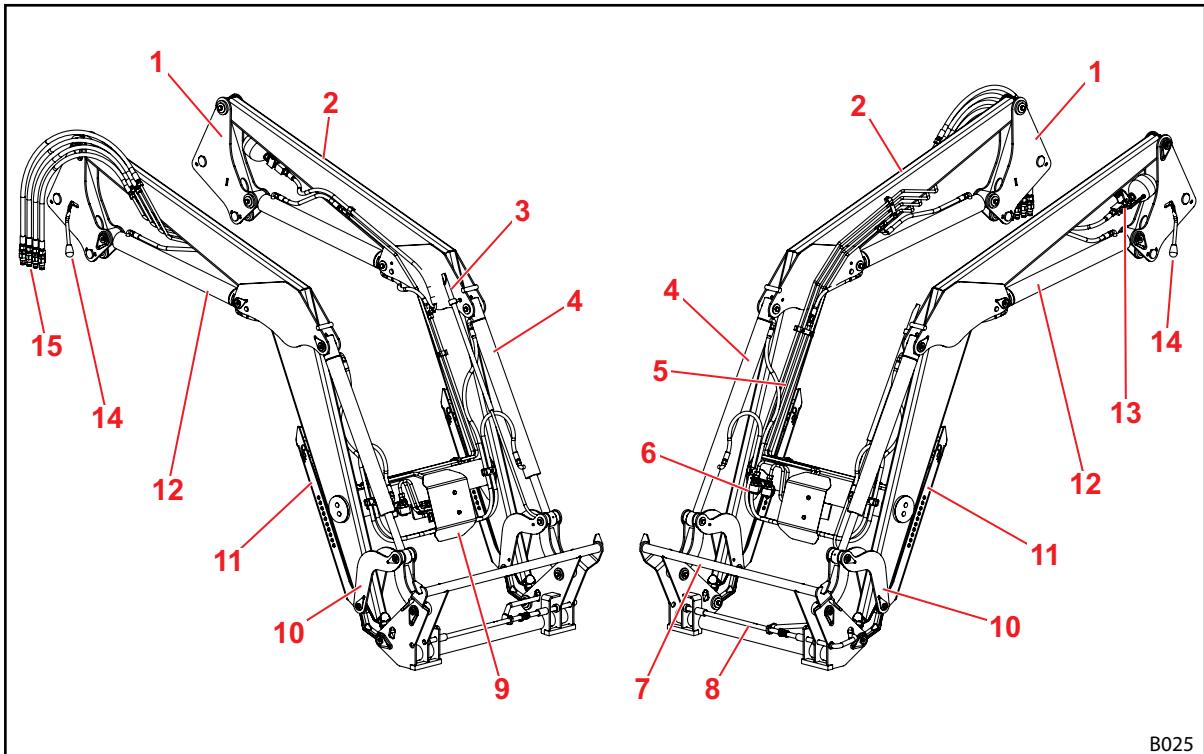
Frontlader H (ohne mechanische Parallelführung)
